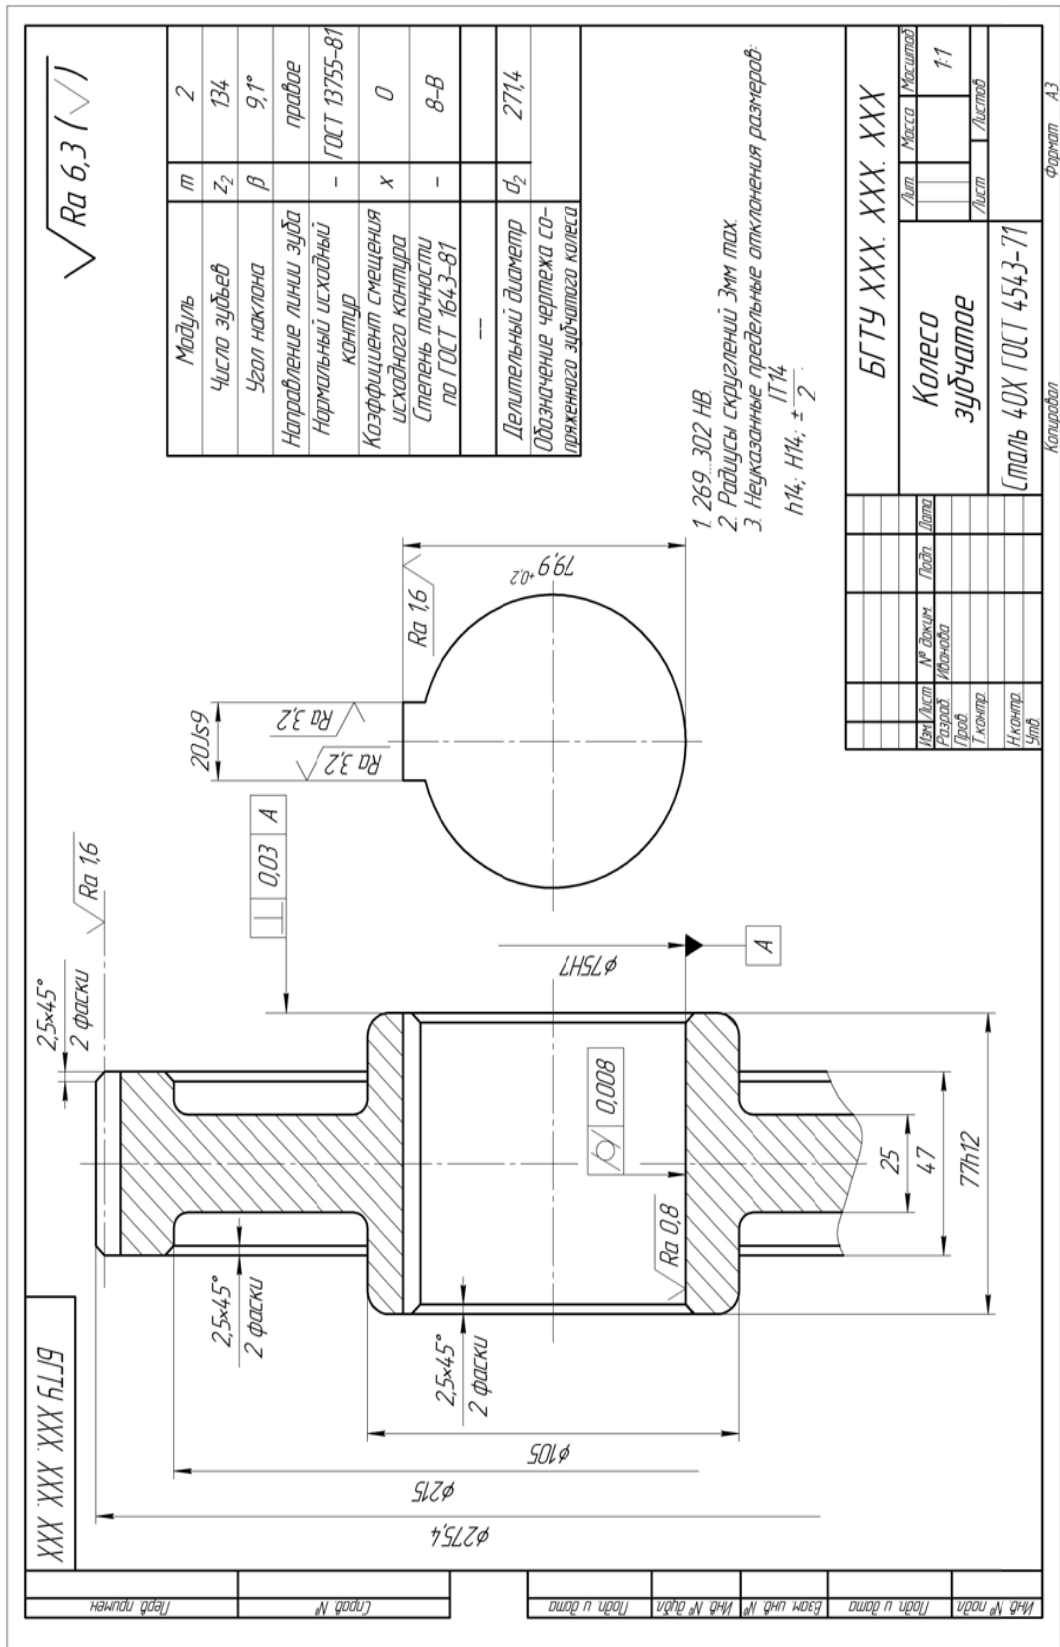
Рабочий чертеж зубчатого колеса редуктора
